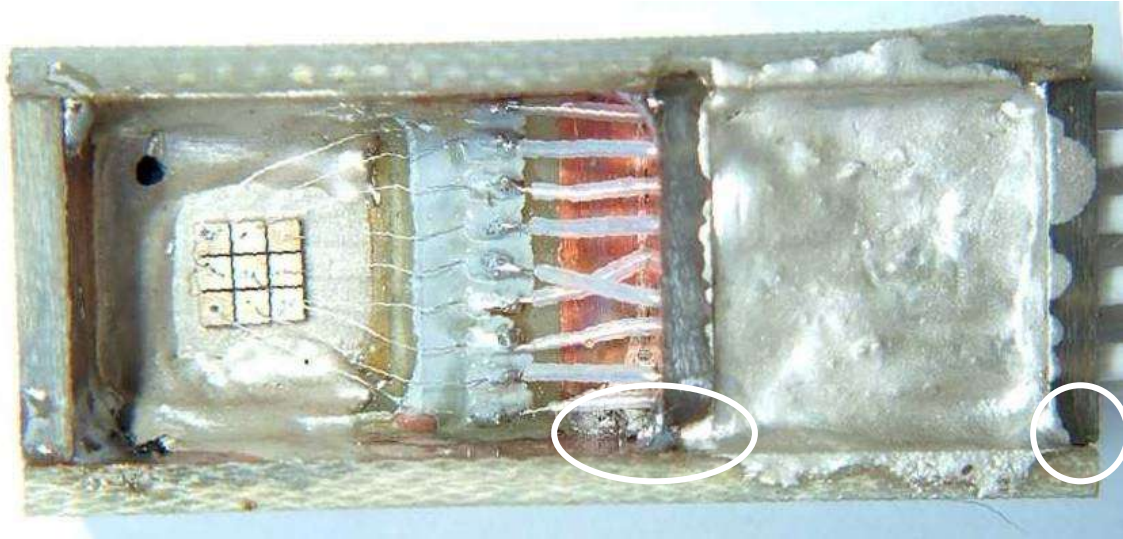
Matriz M1Q. Aspecto da montagem já com as faces laterais soldadas às placas interior e posterior, e a placa anterior soldada às placas laterais e base de encapsulamento. Observar pequeno espaço entre a placa posterior e a lateral inferior. O mesmo acontece entre a placa interior e a lateral inferior. Em ambos os casos a cola não chegou a atravessar. A mancha do que poderia ser a cola derramada junto ao fio inferior é, na verdade, solda entre a placa lateral inferior e a base de encapsulamento.
